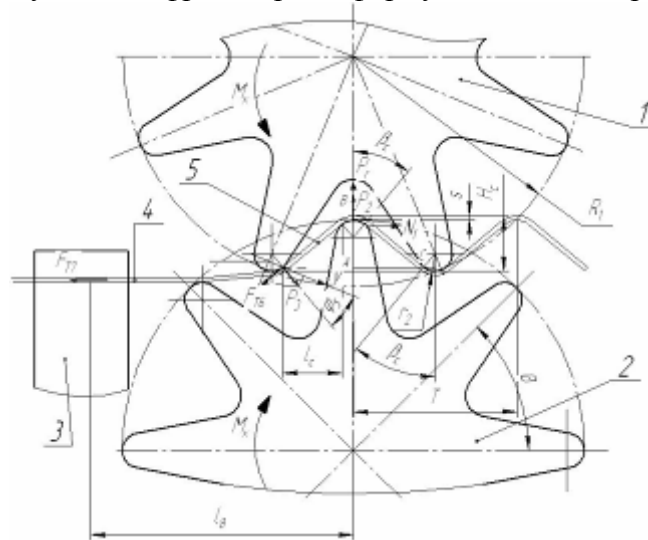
Розрахункова схема процесу формування гофр на стрічці: 1 – верхній формувальний інструмент; 2 – нижній формувальний інструмент; 3 – напрямна; 4 – стрічка; 5 – профільна стрічка
